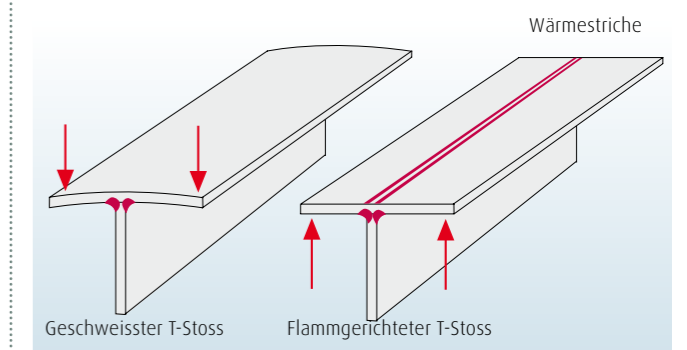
T-Stoss, geschweisst und gerichtet
